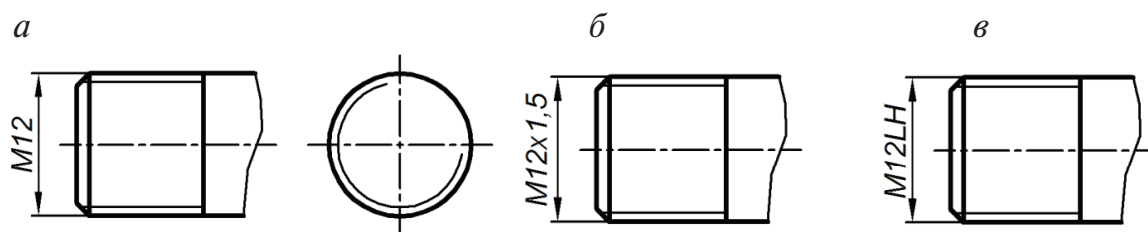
Пример изображения и обозначения на чертеже метрической наружной резьбы (на стержне):
